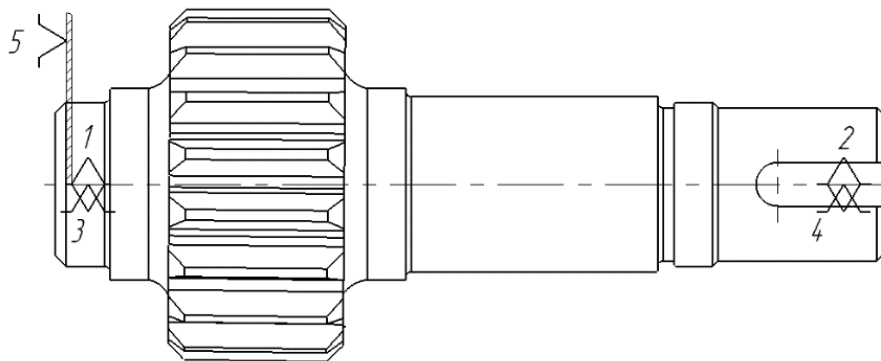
Теоретична схема базування деталі «Вал-шестерня» по загальній технологічній базі (ЗТБ)
